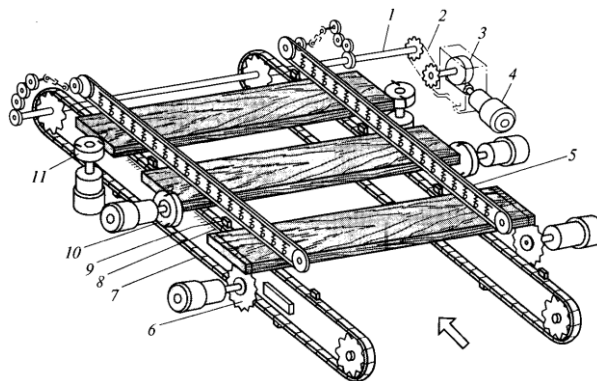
Кінцевирівнювальний верстат з додатковими фрезерними супортами: 1 – вал; 2 – ланцюгова передача; 3 – черв'ячний редуктор; 4 – електродвигун; 5 – притискний ремінь; 6 – пилка; 7 – конвеєрний ланцюг; 8 – напрямна; 9 – упор; 10, 11 – фрези
